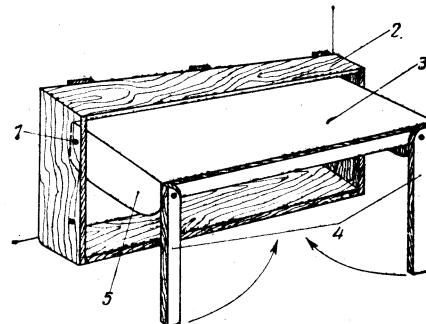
Трансформирующийся низ двухъярусной кровати в положении «стол»: 1 — ось-шарнир; 2 — откидная доска; 3 — столешница; 4 — опорные ножки стола; 5 — боковины (крылья) стола
